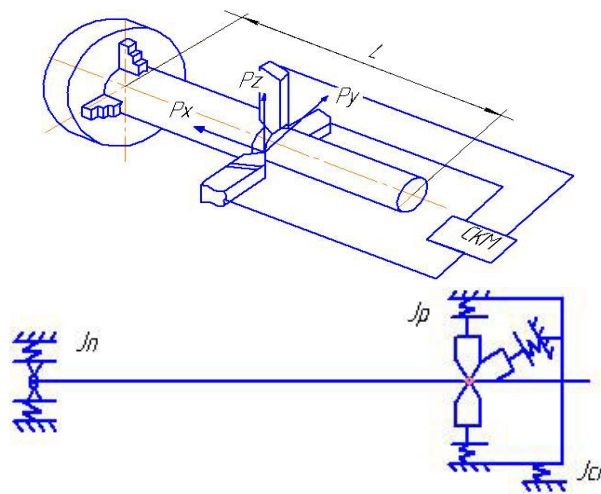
Схема обробки циліндричної деталі трирізцевою головкою
